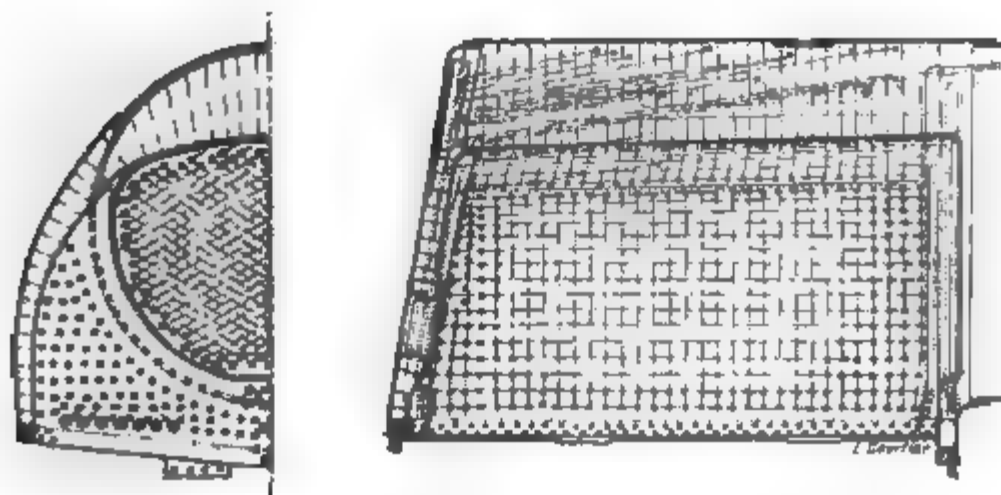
Foyer Wooten pour locomotive à anthracite type 2-8-0 du D. & H.
